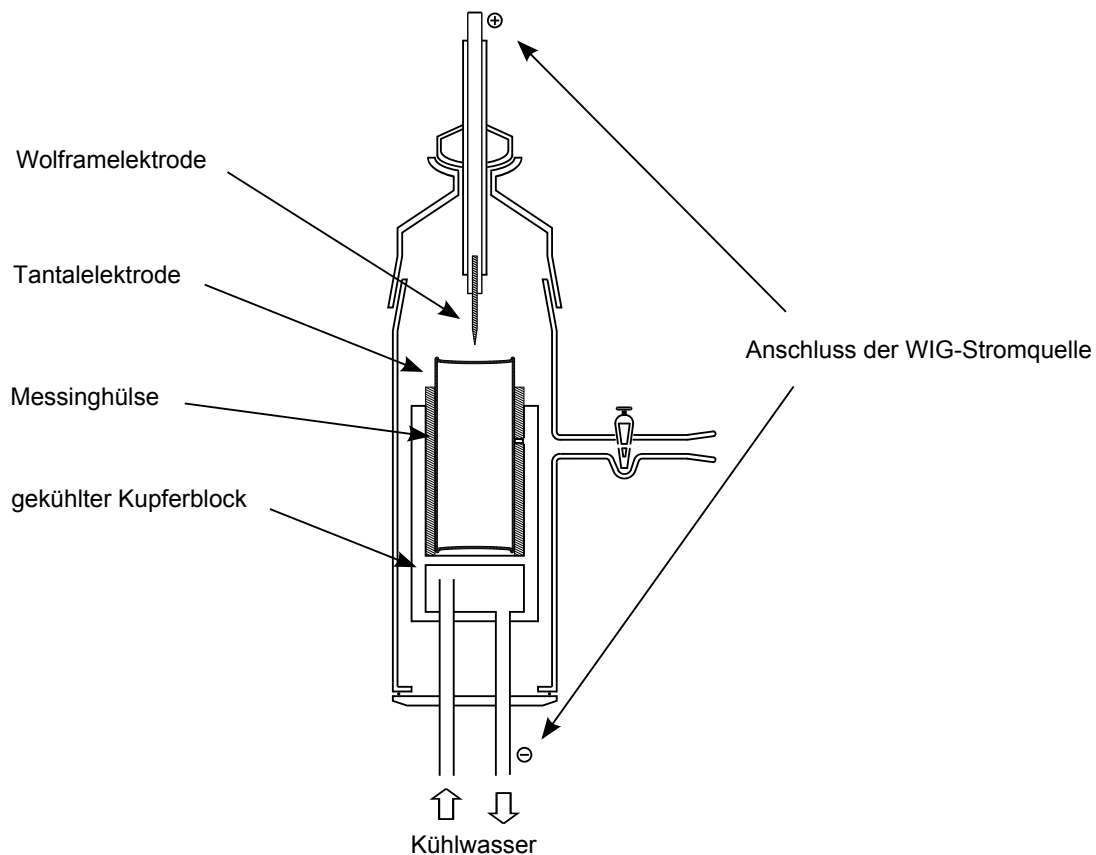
Apparatur zum Wolfram-Inertgasschweißen von Tantalampullen
